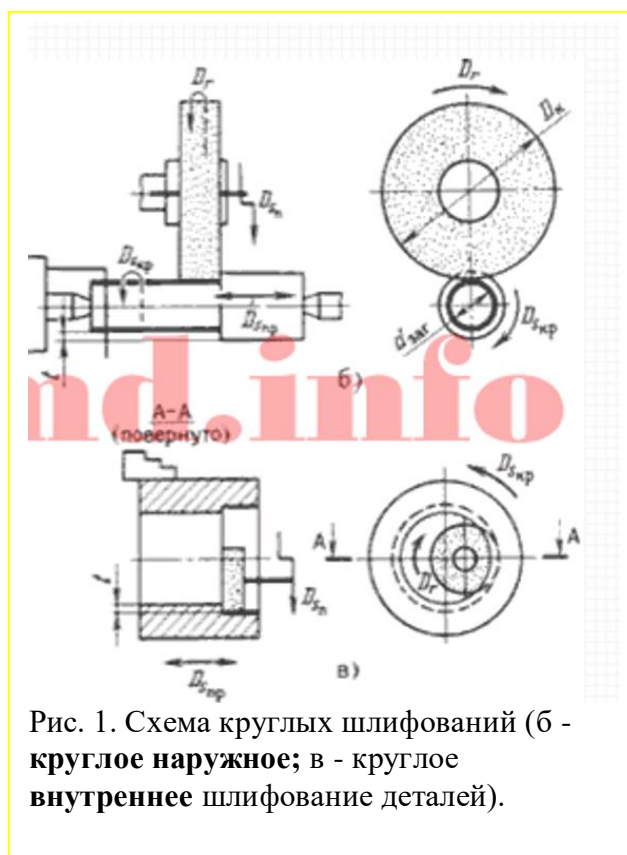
Схема круглых шлифований (б - круглое наружное; в - круглое внутреннее шлифование деталей).
